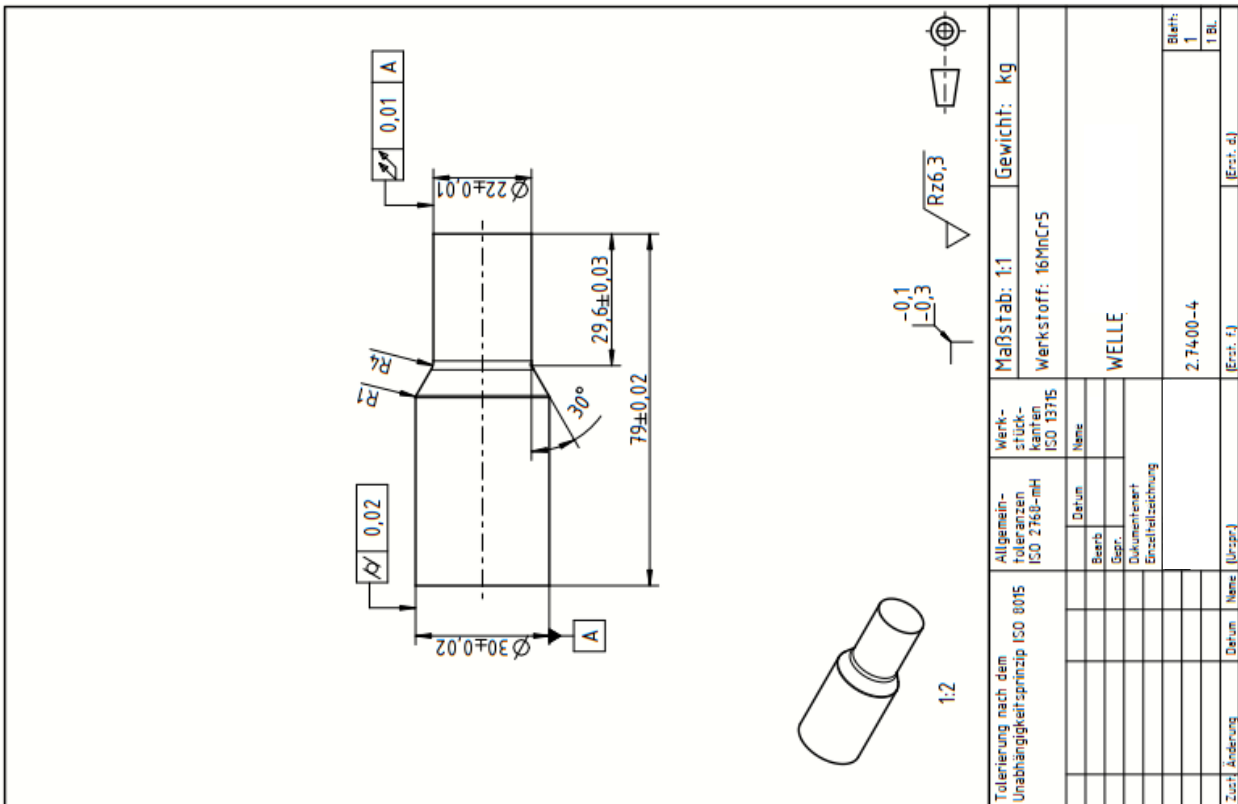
Fertigungszeichnung der einfach abgesetzten Welle zum Umformfügen
